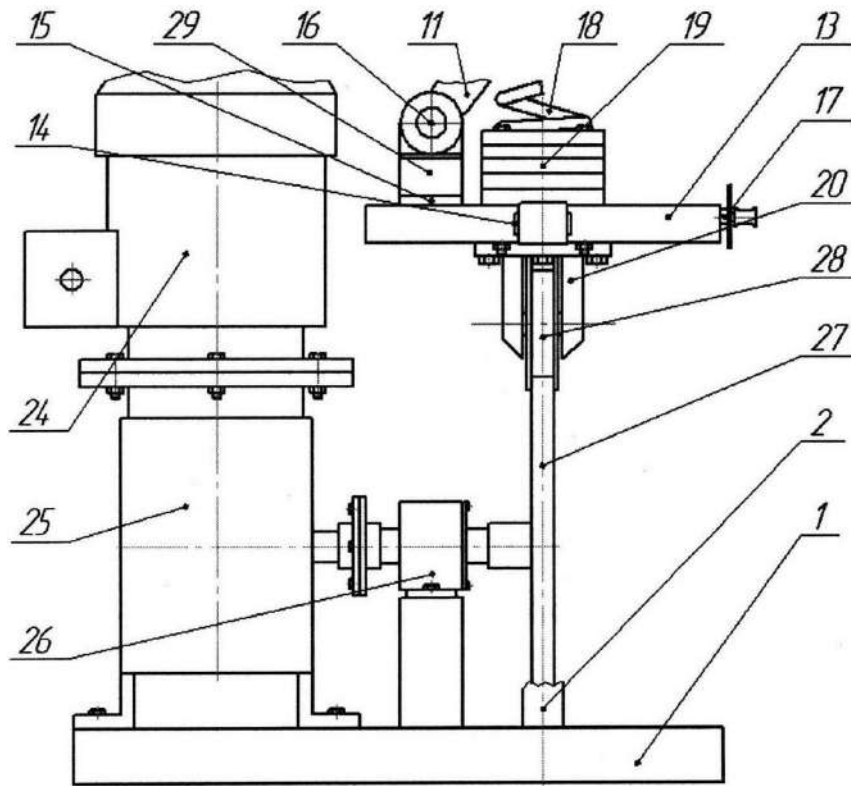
Креслення ексцентрика, вид збоку
